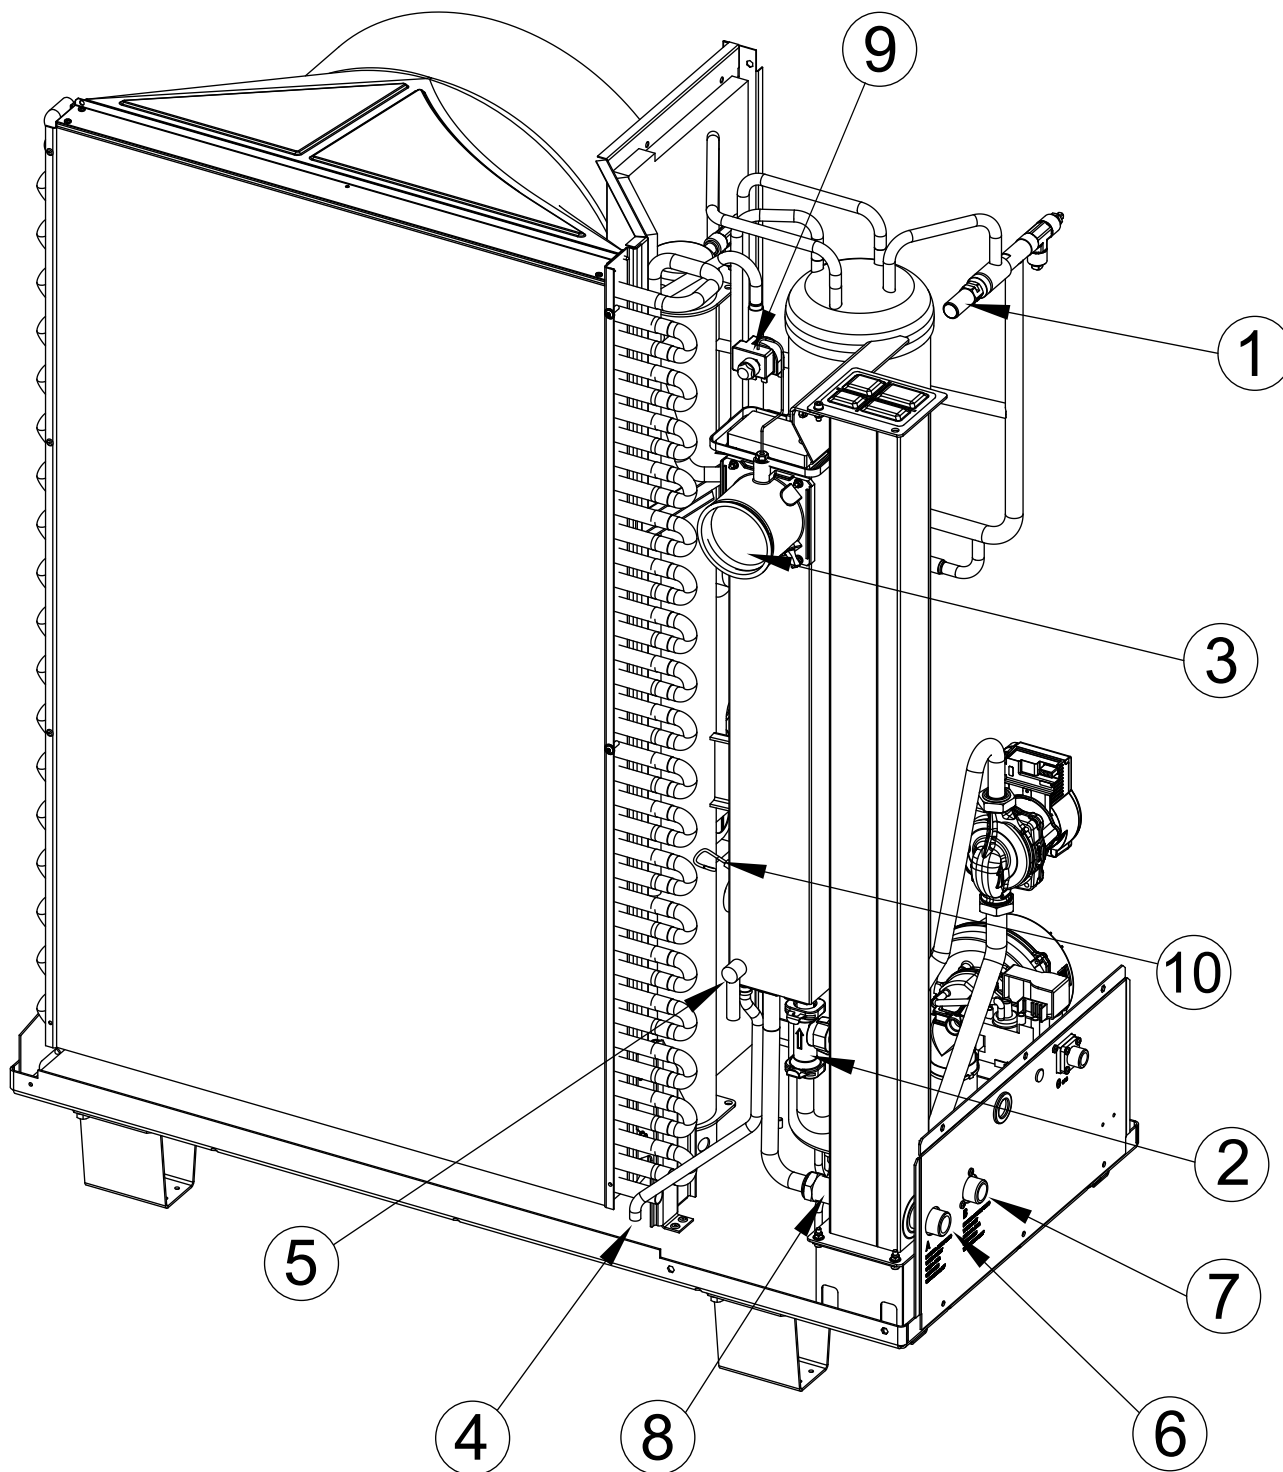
Componenti interni modulo pompa di calore vista frontale sinistra
